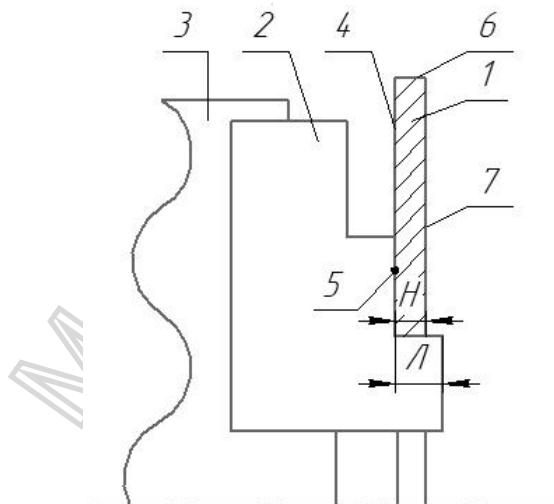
Схема базирования и закрепления заготовки детали «Фланец».
